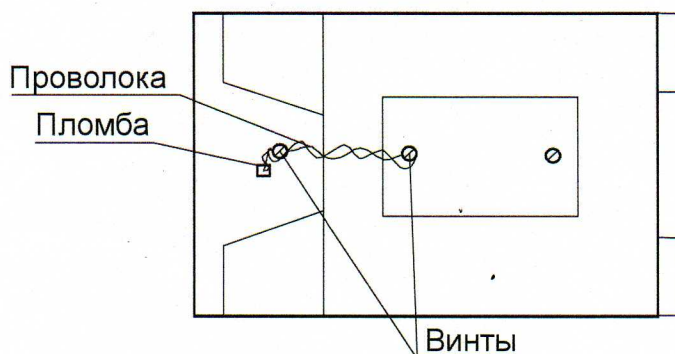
Схема пломбировки вторичного преобразователя при креплении на DIN-рейку.
